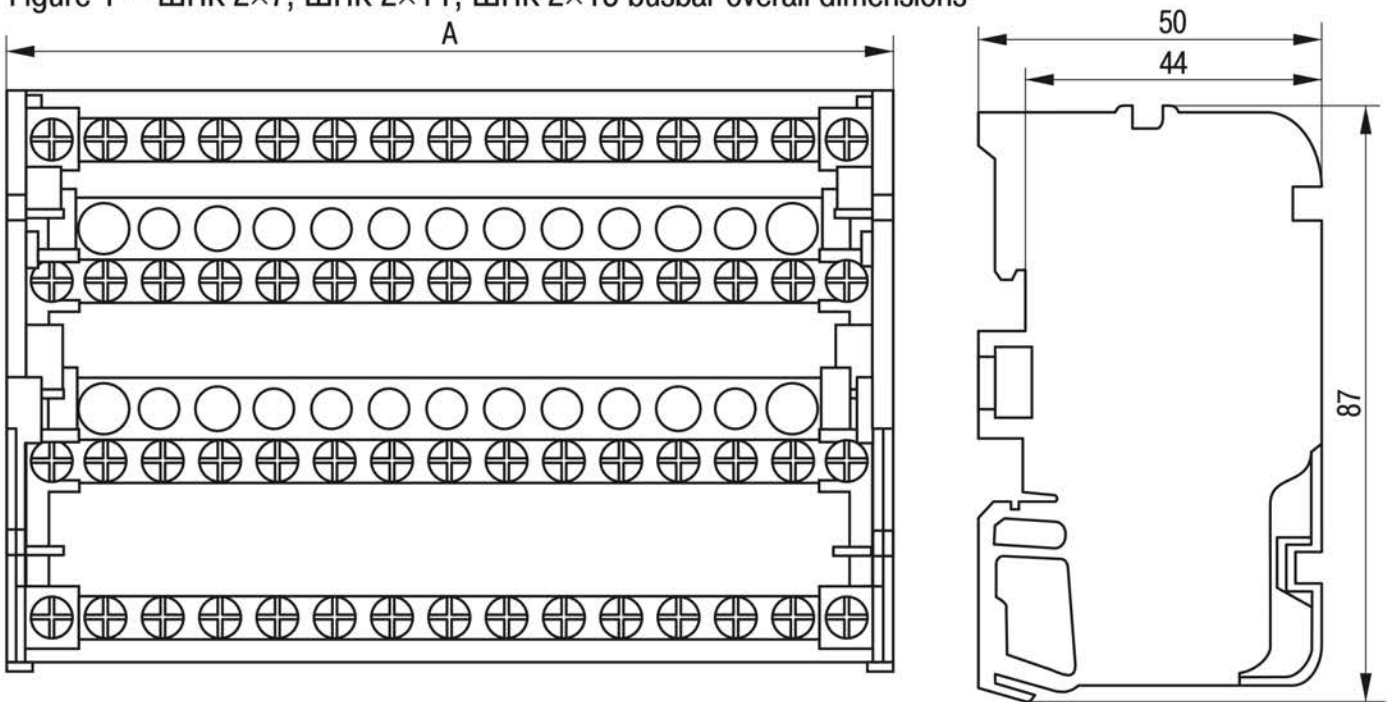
Габаритные размеры шин ШНК 4×7, ШНК 4×11 и ШНК 4×15 /
